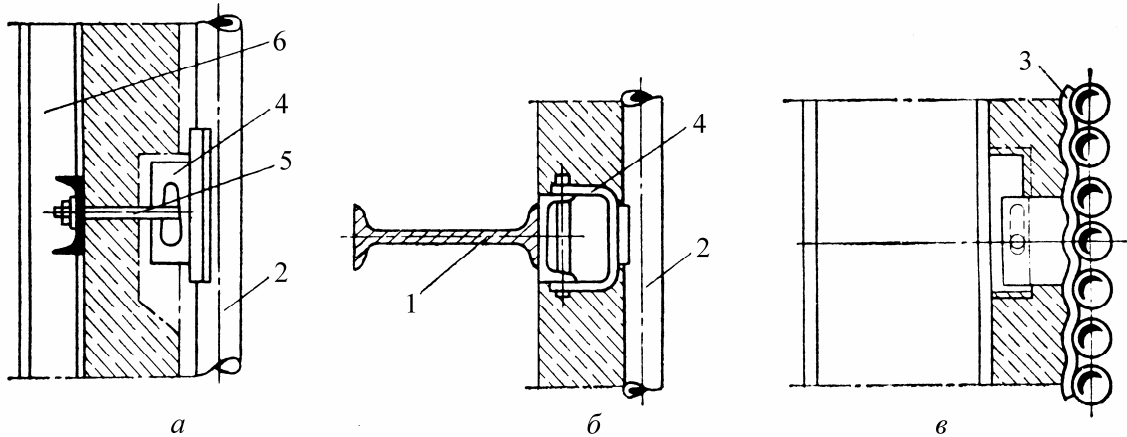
Способы крепления экранных труб: *а* – крепление к балке каркаса; *б* и *в* – крепление к горизонтальной балке, перемещающейся вместе с трубами; 1 – балка; 2 – экранные трубы; 3 – планки, приваренные к трубам; 4 – скоба; 5 – тяга; 6 – балка каркаса
